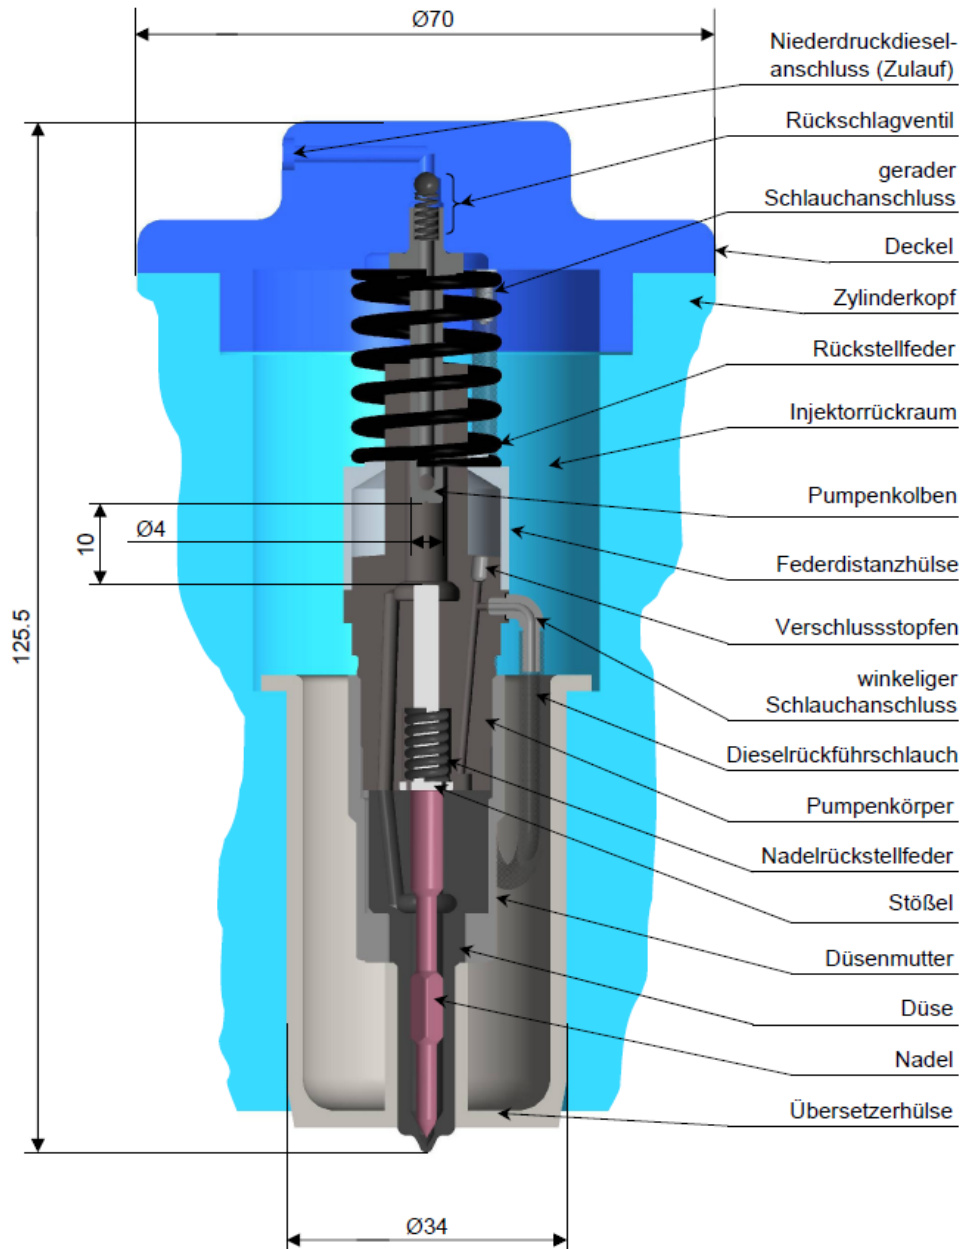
Schnitt des Konstruktionsvorschlags mit den Hauptabmessungen
